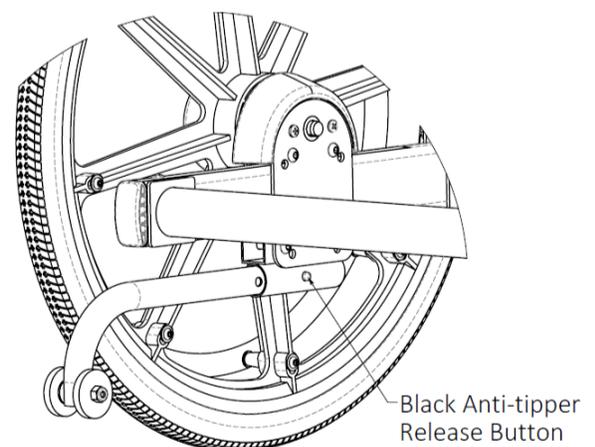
Installazione dell'anti-ribaltamento posteriore
